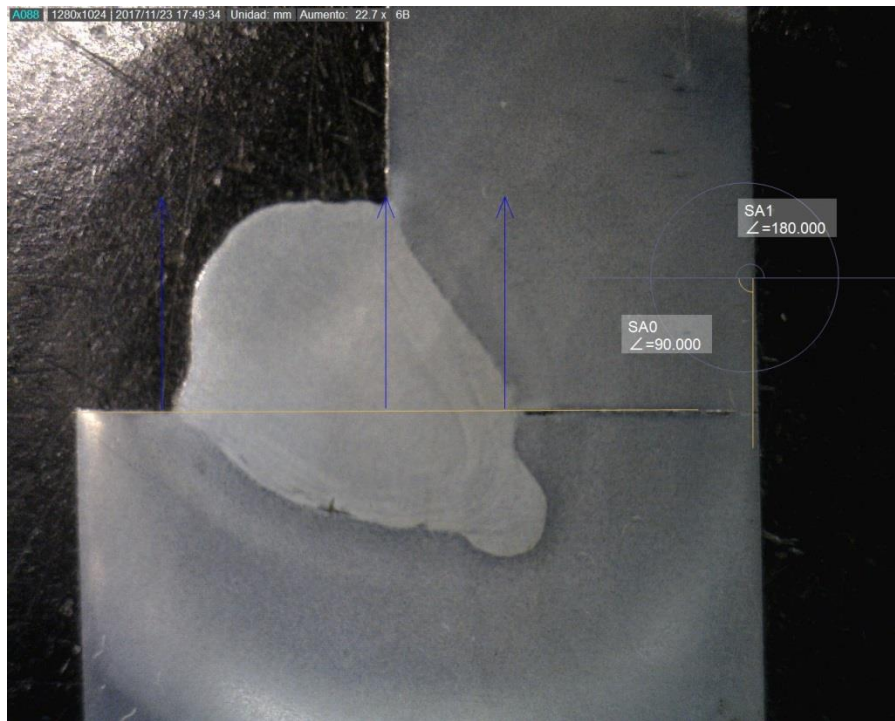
13 Perfil obtenido en cupón de soldadura 7A.
